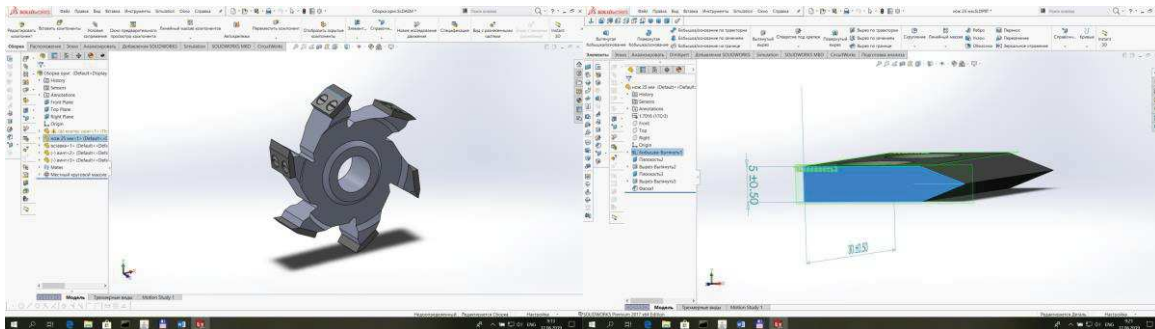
Трехмерная геометрическая твердотельная модель эффективной фрезы, сформированная в пакете SolidWorks, и ножа с наноразмерной вставкой
